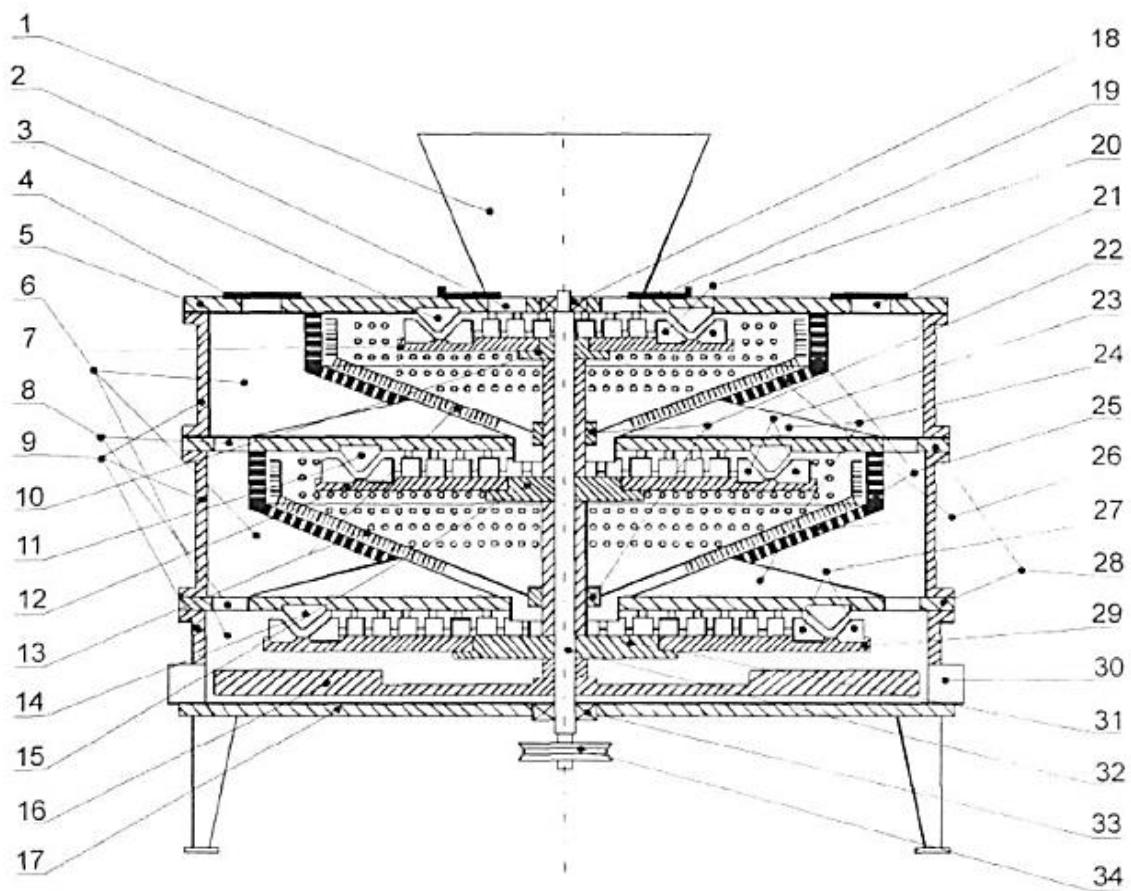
Багатоступінчастий подрібнювач фуражного зерна: 1 – завантажувальний бункер; 2 – завантажувальні вікна; 3, 11, 14 – робочі органи статора; 4 – кільцева заслінка; 5 – верхня торцева плита; 6 – за решітний простір; 7, 12, 29 – диска; 8 – кришки; 9 – збірний циліндричний корпус; 10, 15, 31 – маточини; 13 – очисні щітки; 16 – крилач; 17 – нижня торцева плита; 18, 33 – корпуси; 19 – регулююча заслінка; 20, 23 і 27 – робочі органи ротора-диска; 21 – регулювальні вікна; 22 – хомути; 24 – скатні дошки; 25 – решето-матриця; 26 – конусна воронка; 28 – статори; 30 – відвідні патрубки; 32 – вертикальний вал; 34 – шків.
